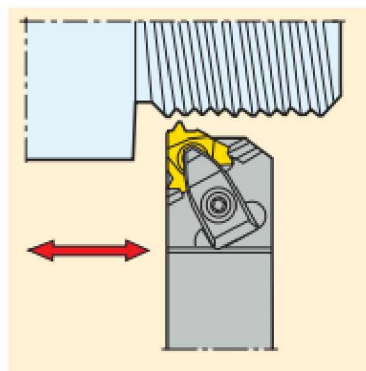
Різець для зовнішньої обробки з ромбічною пластиною ER
